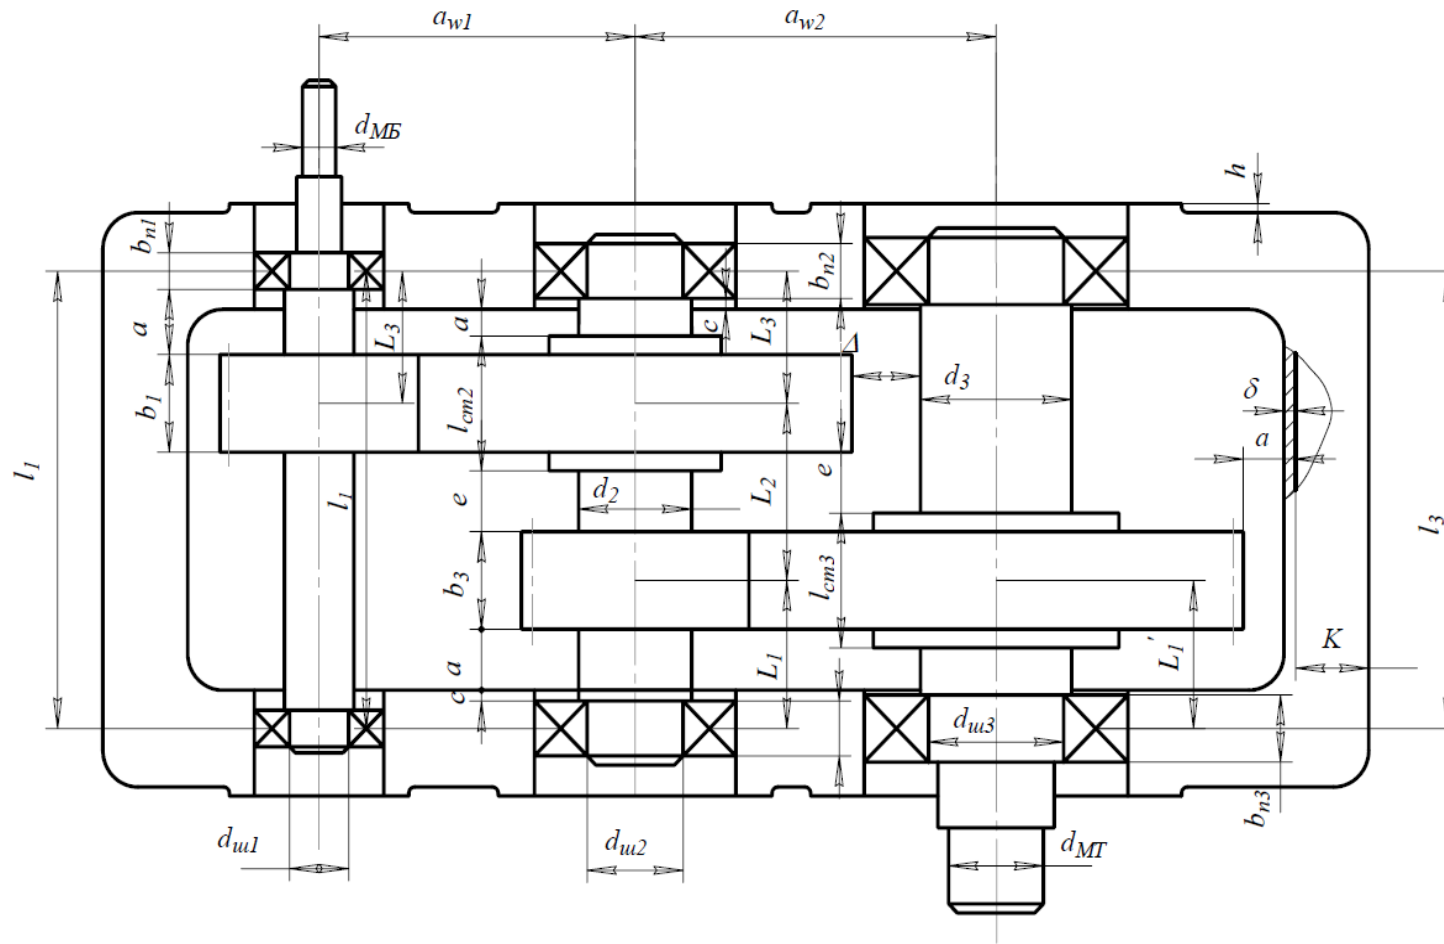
Ескізне компонування двоступінчастого циліндричного редуктора
